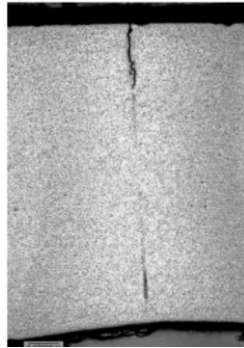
Falta de fusión en el eje de la soldadura.
